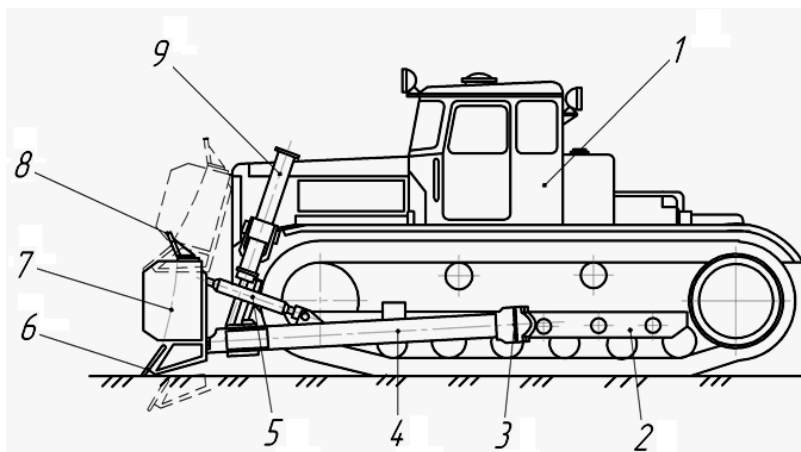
Конструктивна схема бульдозера з неповоротним відвалом: 1 - базовий трактор; 2 - ходові колеса; 3 - упряжні шарніри; 4 - штовхаючі бруси; 5 - підкоси; 6 - ножі; 7 - відвал; 8 - козирьок; 9 - гідроциліндри
